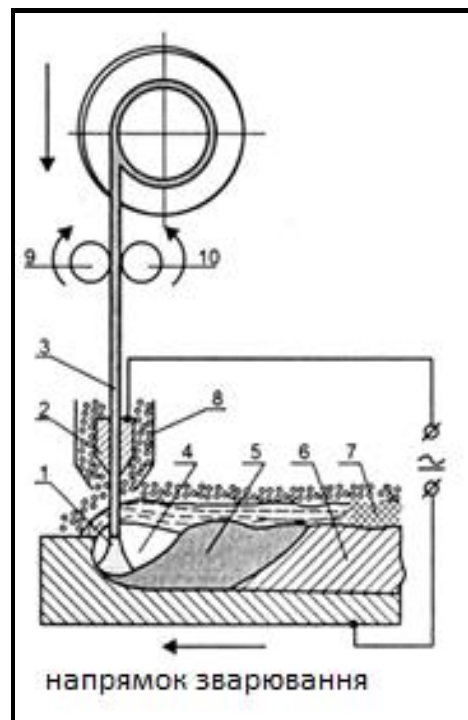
Схема зварювання під шаром флюсу: 1 – дуга; 2 – флюс; 3 – електричний дріт; 4 – газовий простір; 5 – рідкий метал; 6 – основний метал; 7 – поверхневий шар; 8 – мундштук; 9 – ведучий механізм; 10 – притискний механізм
